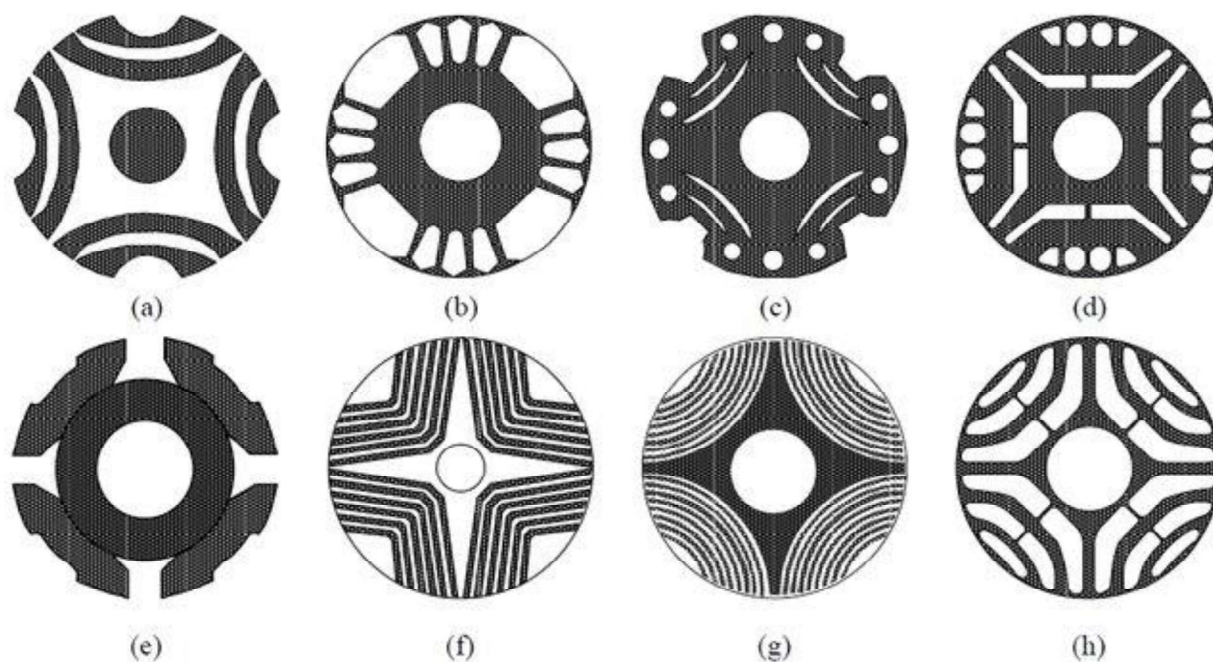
Evolução do MSR no desenvolvimento de diferentes estruturas de rotor. (a) rotor Kostko original; (b) rotor adaptado de um motor de indução; (c) rotor com múltiplas barreiras; (d) rotor com segmentos saturáveis; (e) rotor segmentado; (f) rotor laminado axialmente em 'V'; (g) rotor laminado axialmente em 'U'; (h) rotor moderno laminado transversalmente. (adaptado [7])
